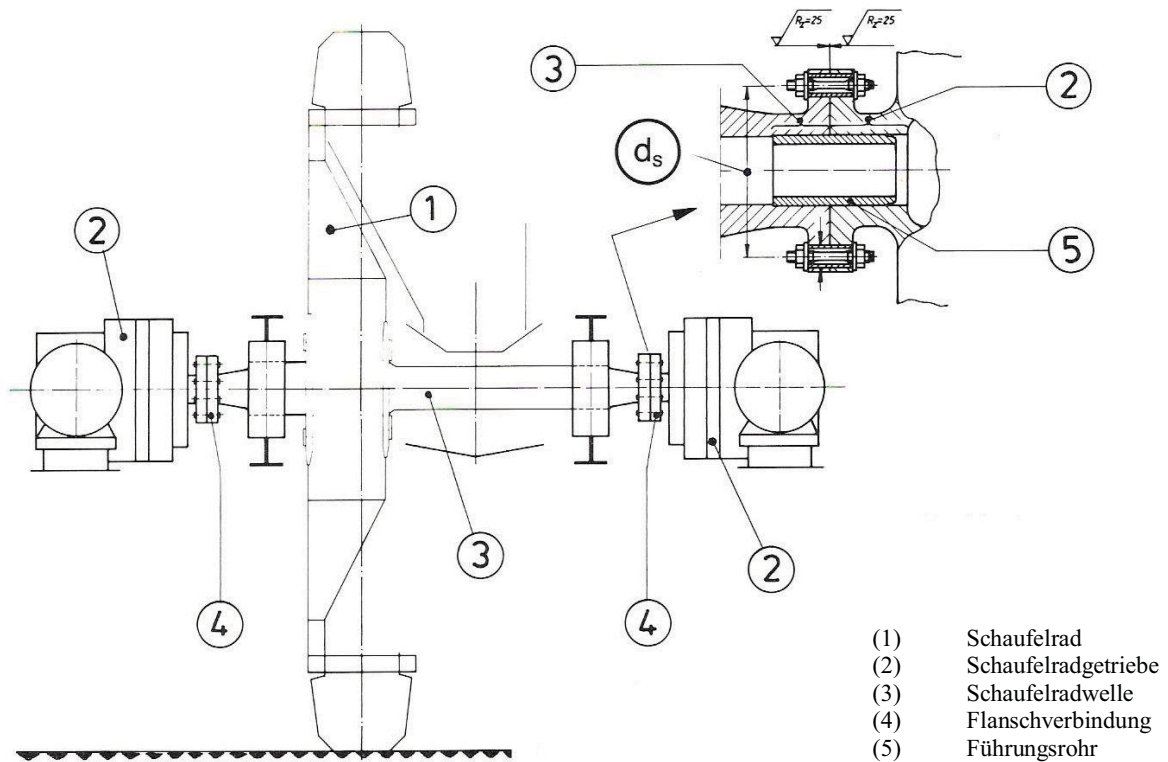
Flanschverbindung zwischen Schaufelradwelle und Getriebegroßrad
